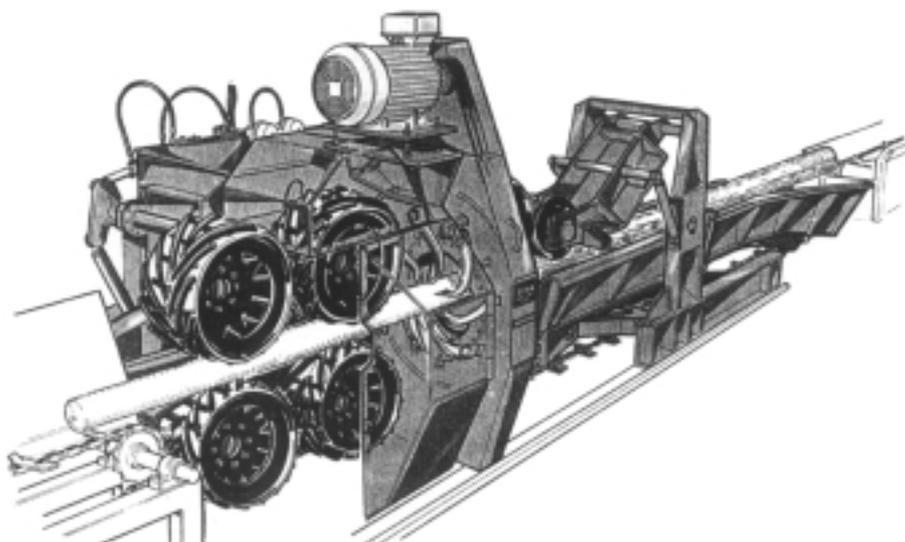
Écorceuse à rotor mobile verticalement et entraînement des bois par chenille crantée et diablo (Cliché Sté ESTERER)
